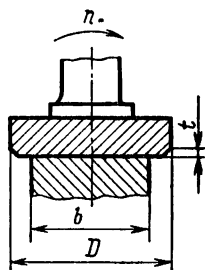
Схема фрезерования плоской поверхности торцовой фрезой
